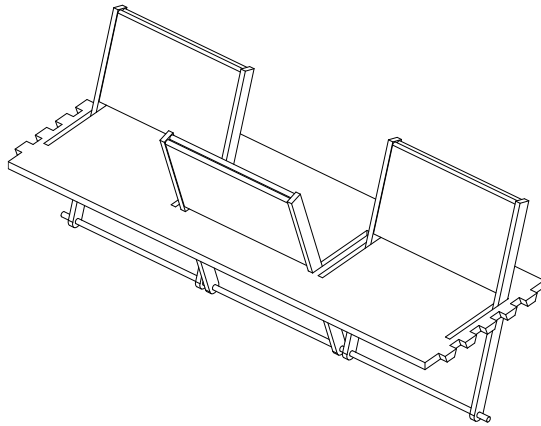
Esquema montaje conjunto 1 (elaboración propia, 2025)
